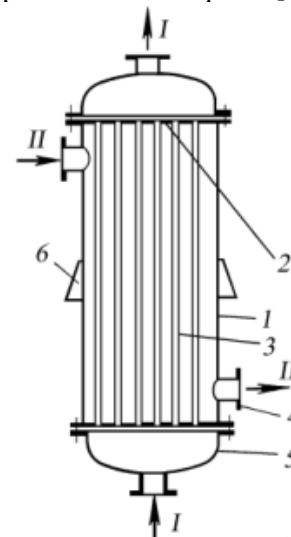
Вертикальний кожухотрубний теплообмінник з нерухомими трубними ґратами: 1 – кожух; 2 – трубна решітка; 3 – труби; 4 – патрубок; 5 – кришка; 6 – опорна лапа; I, II – теплоносії
